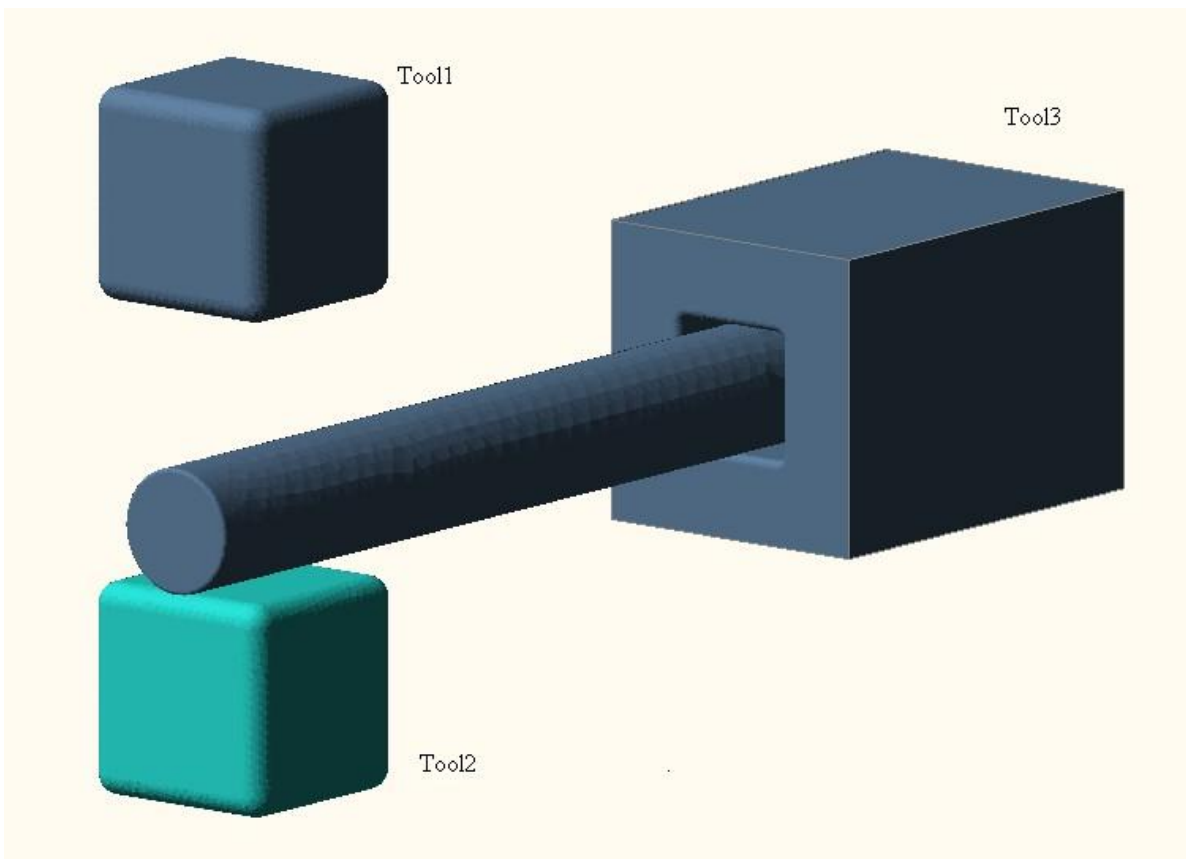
Расчётная модель из заготовки и трёх инструментов
